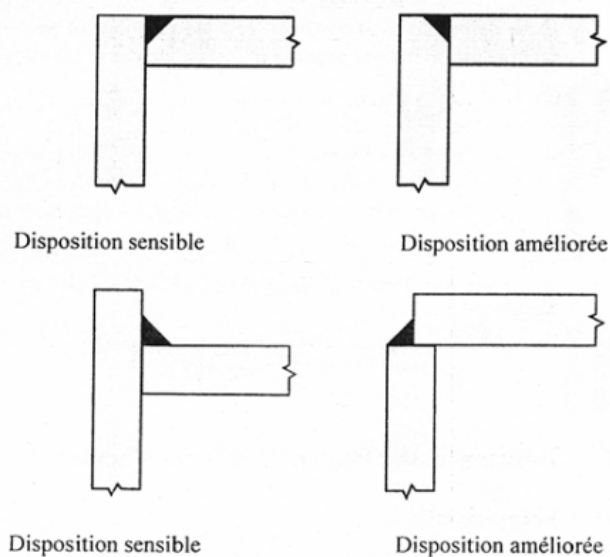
Dispositions constructives évitant l'arrachement lamellaire
